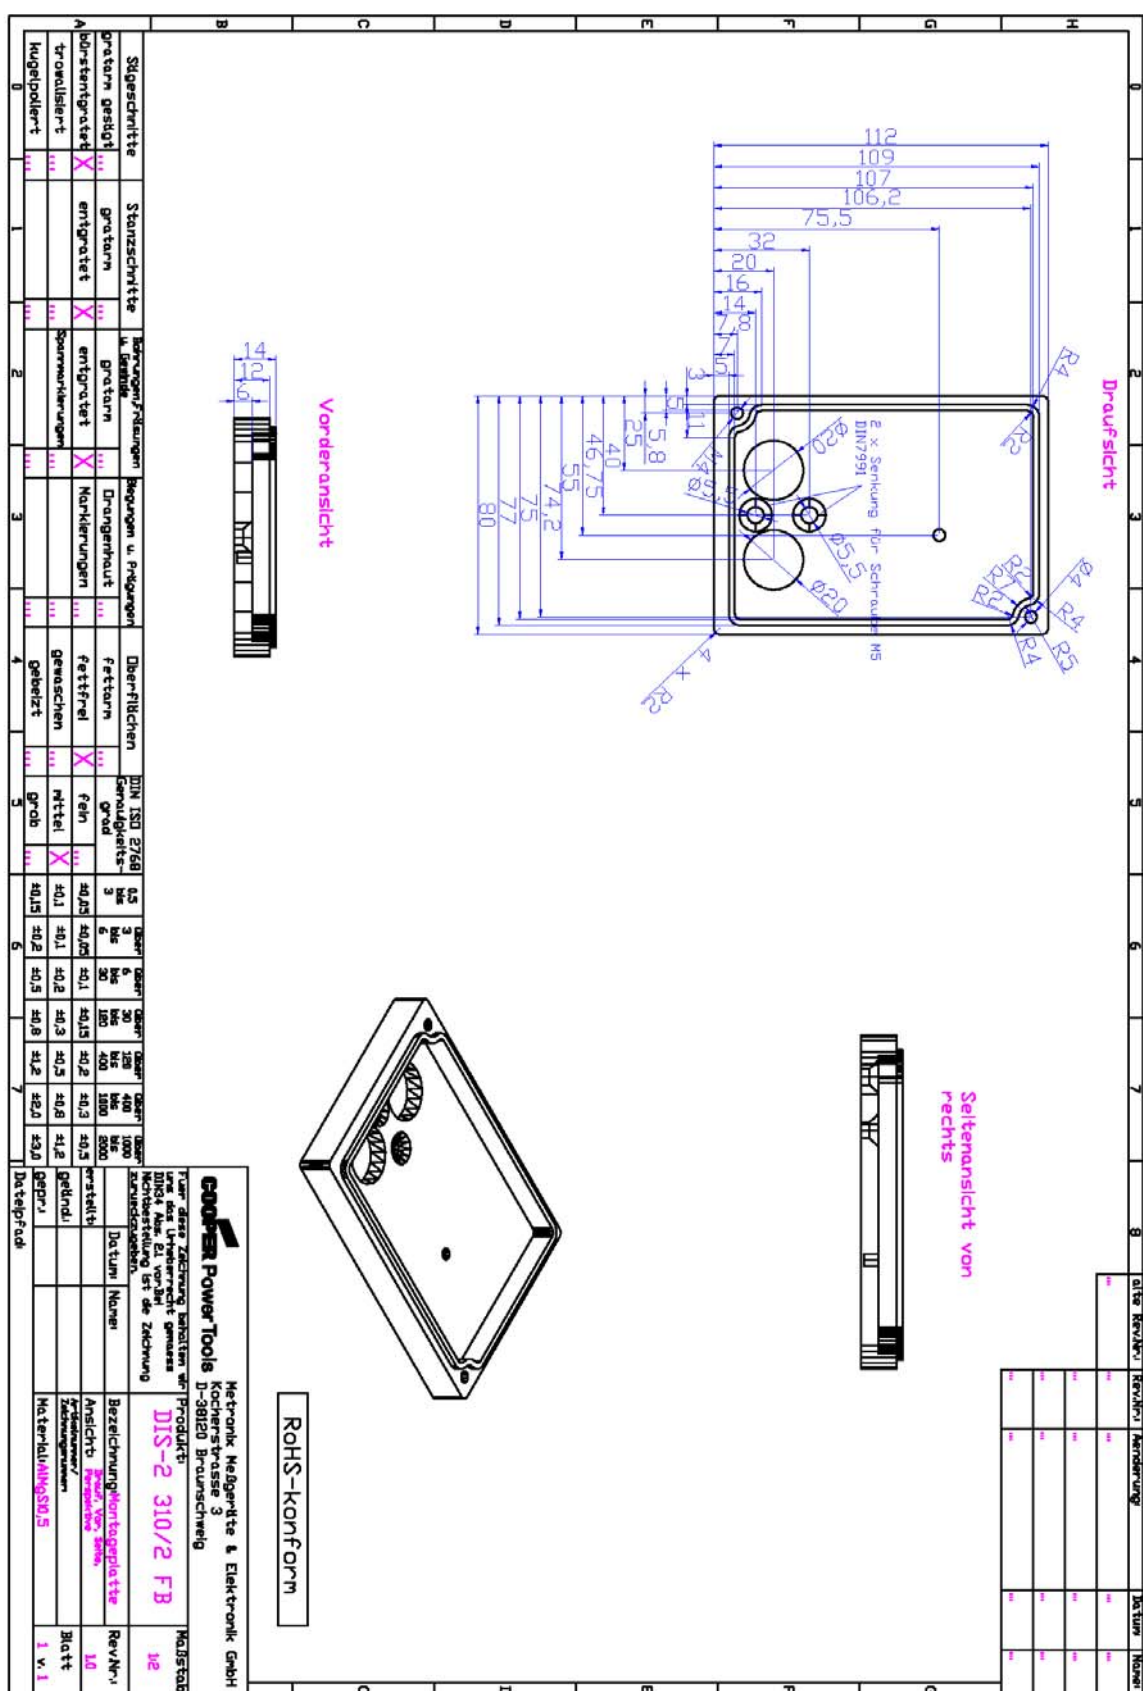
Beispiel einer Montageplatte auf einem Motor
